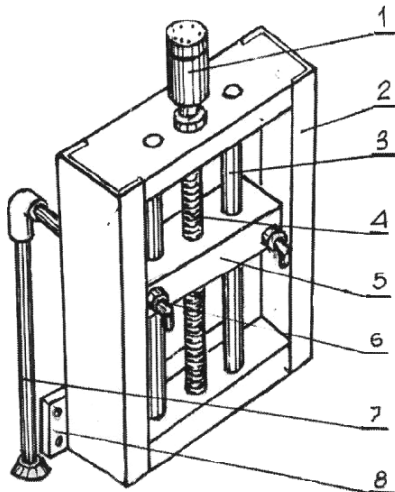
Схема загального виду механізму підйому заготовок: 1 – кроковий двигун; 2 – рама; 3 – напрямні валики; 4 – ходовий гвинт; 5 – траверс; 6 – штуцер; 7 – арматура; 8 – пластик
